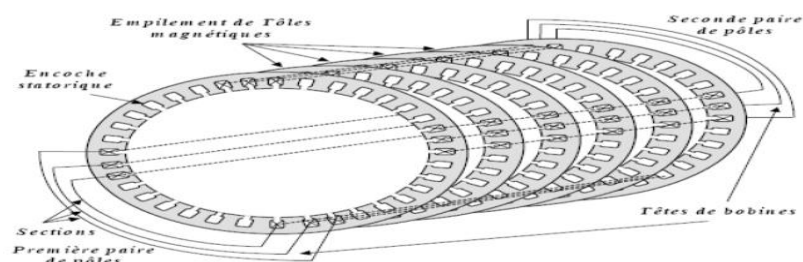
Forme éclaté d'un moteur à rotor à cage.
